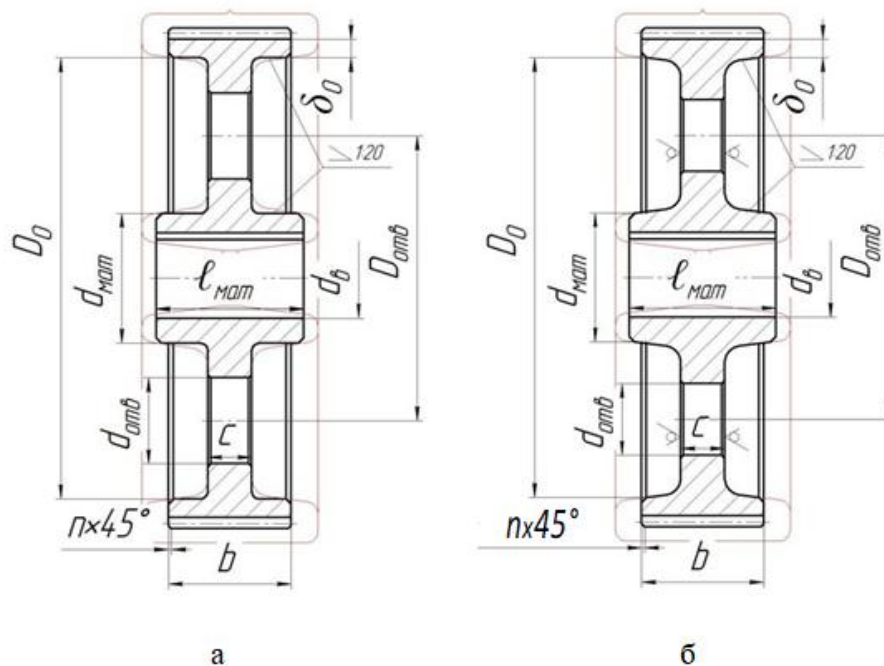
Конструкція циліндричного зубчастого колеса виготовленого за допомогою двосторонніх штампів
